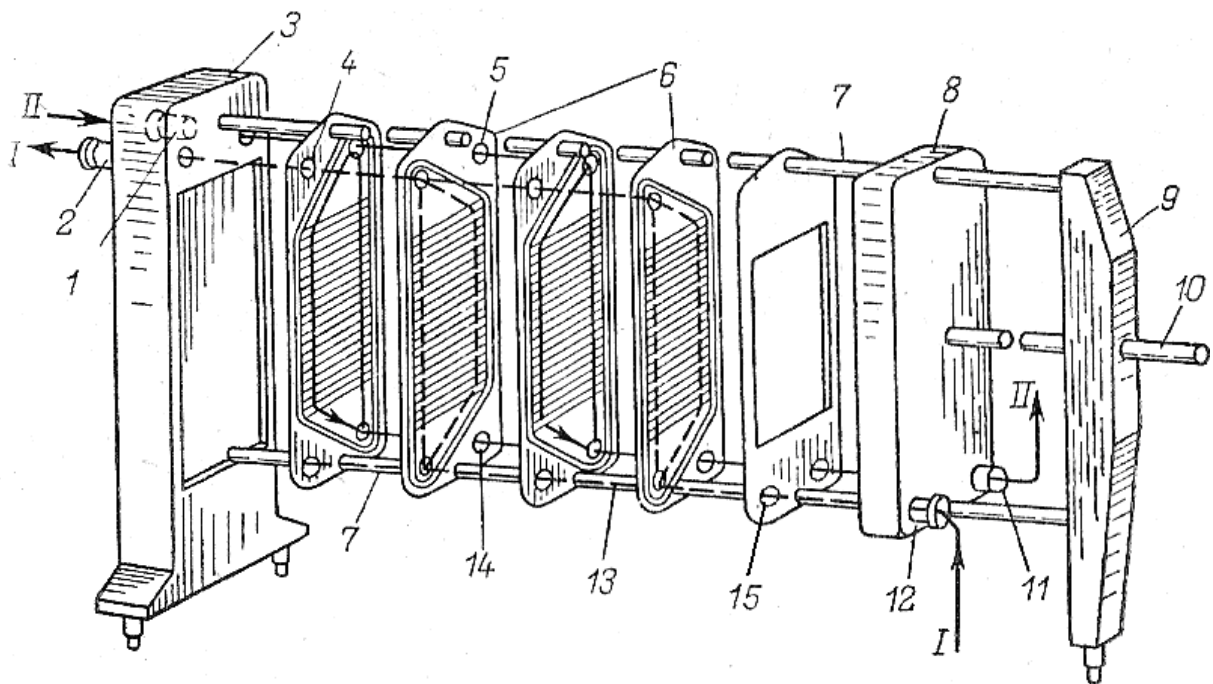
9. Разборный пластинчатый теплообменник типа «фильтр-пресс»:
